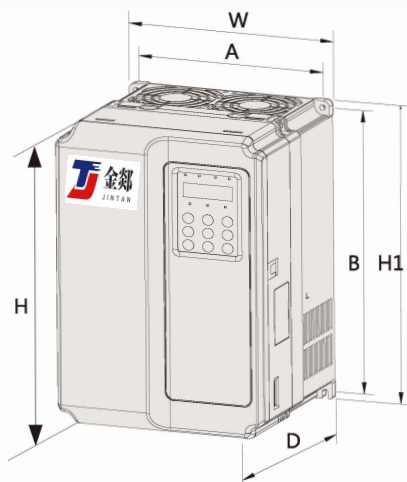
HK900系列 塑胶结构外型尺寸及安装尺寸示意图
